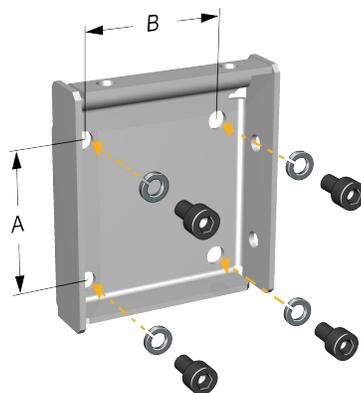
Монтажный кронштейн для крепления преобразователя в корпусе из нержавеющей стали
